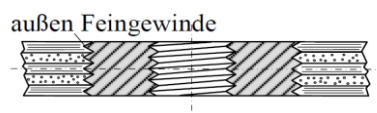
Insert als Gewindeeinsatz (schräg schraffiert) wird direkt in das Laminat verschraubt. In das Innengewinde werden gewählte Befestigungselemente eingeschraubt, [Sch07]
